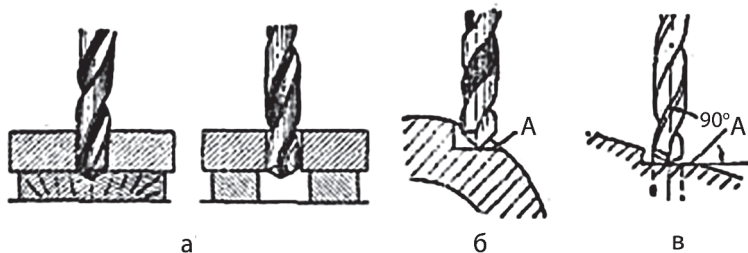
Сверление отверстий насквозь (а), на цилиндрической (б) и наклонной поверхностях (в)
